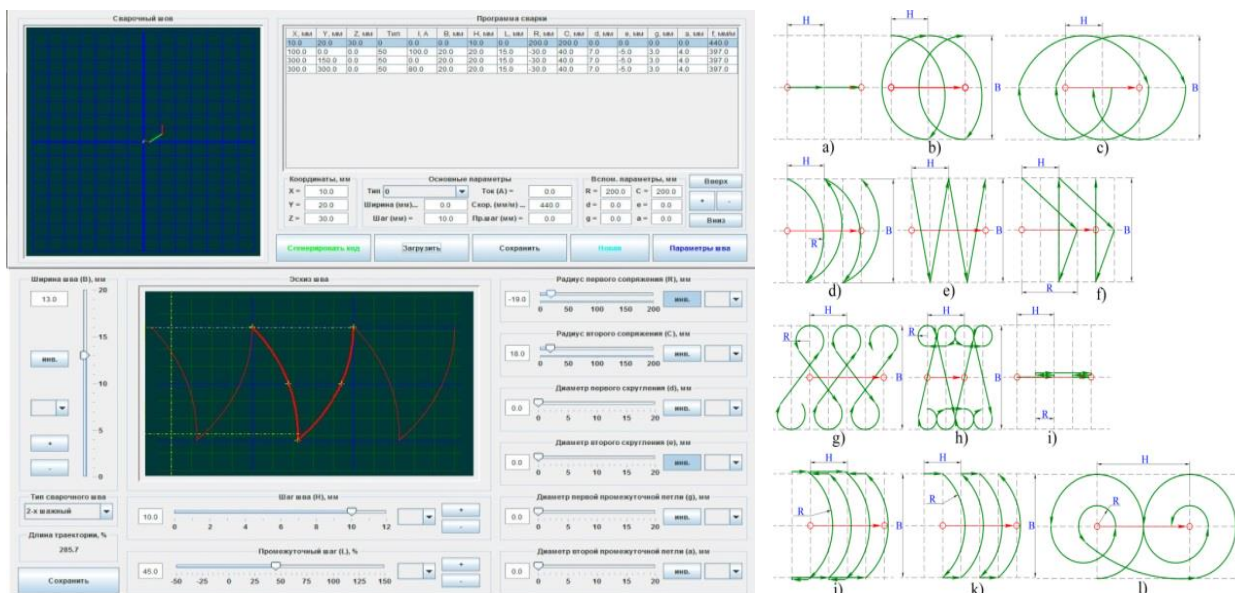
Интерфейс разрабатываемого приложения и схемы движения сварочного сопла под управлением G-кодов
